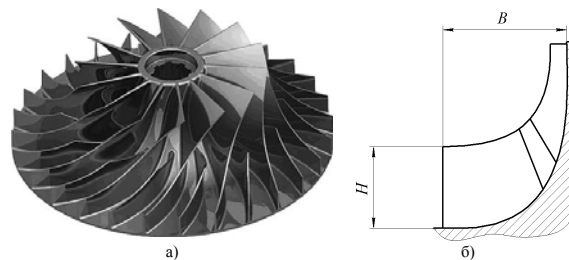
Общий вид центробежного моноколеса и эскиз лопатки
